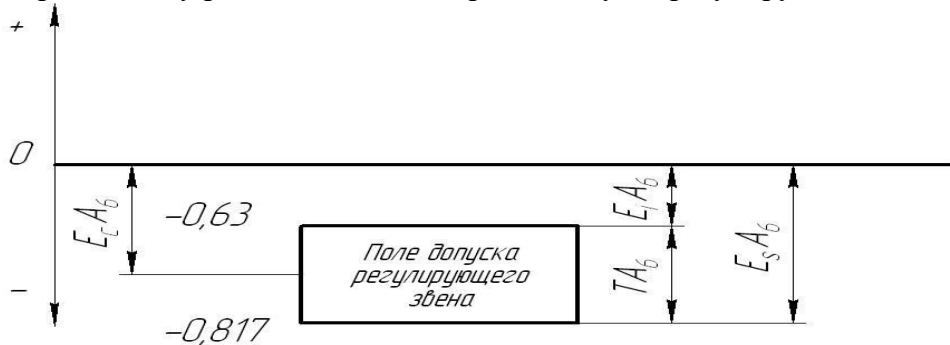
Схема расположения интервала допуска регулирующего звена
